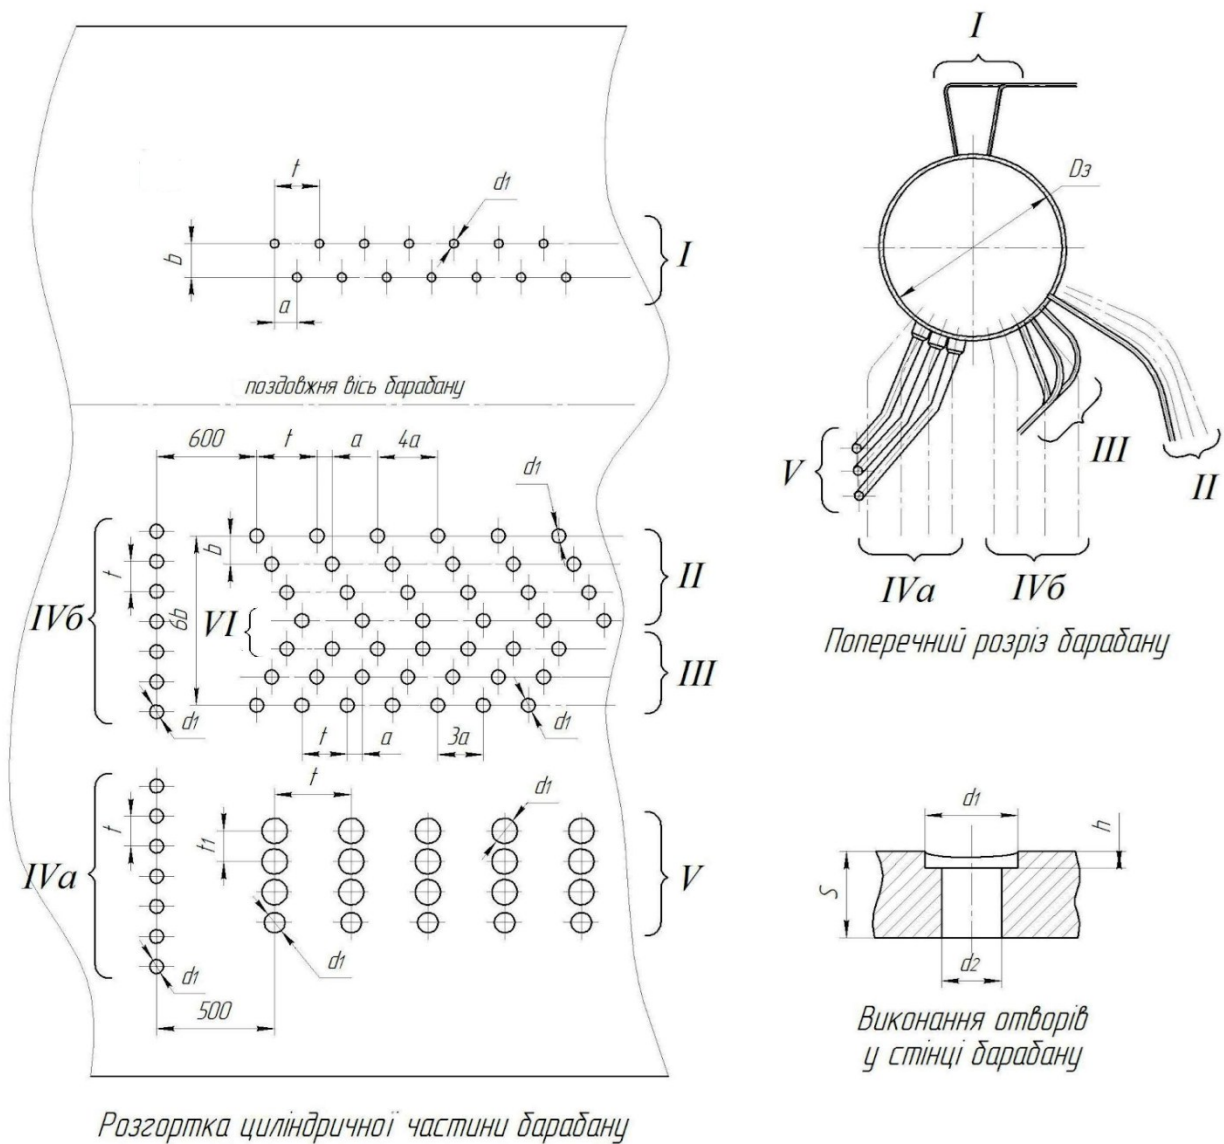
Розгортка циліндричної частини барабану котла БКЗ-75-39 ФБ і розташування груп отворів.
